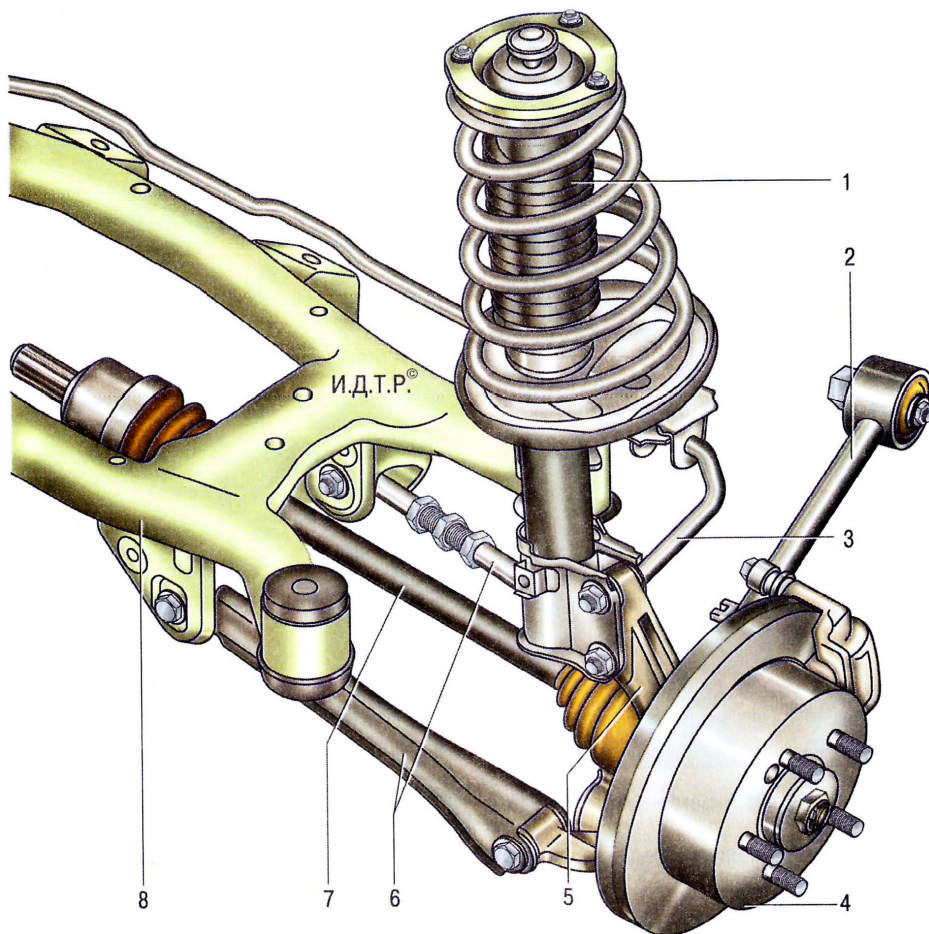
Задняя подвеска (правая сторона): 1 – амортизаторная стойка; 2 – продольный рычаг; 3 – стабилизатор поперечной устойчивости; 4 – тормозной механизм; 5 – кулак со ступицей; 6 – поперечные рычаги; 7 – привод заднего колеса; 8 – подрамник
